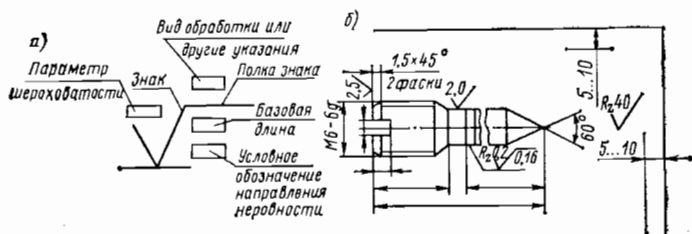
Условные обозначения шероховатости: а — форма знака шероховатости; б — место расположения знака и обозначение шероховатости на чертеже детали
